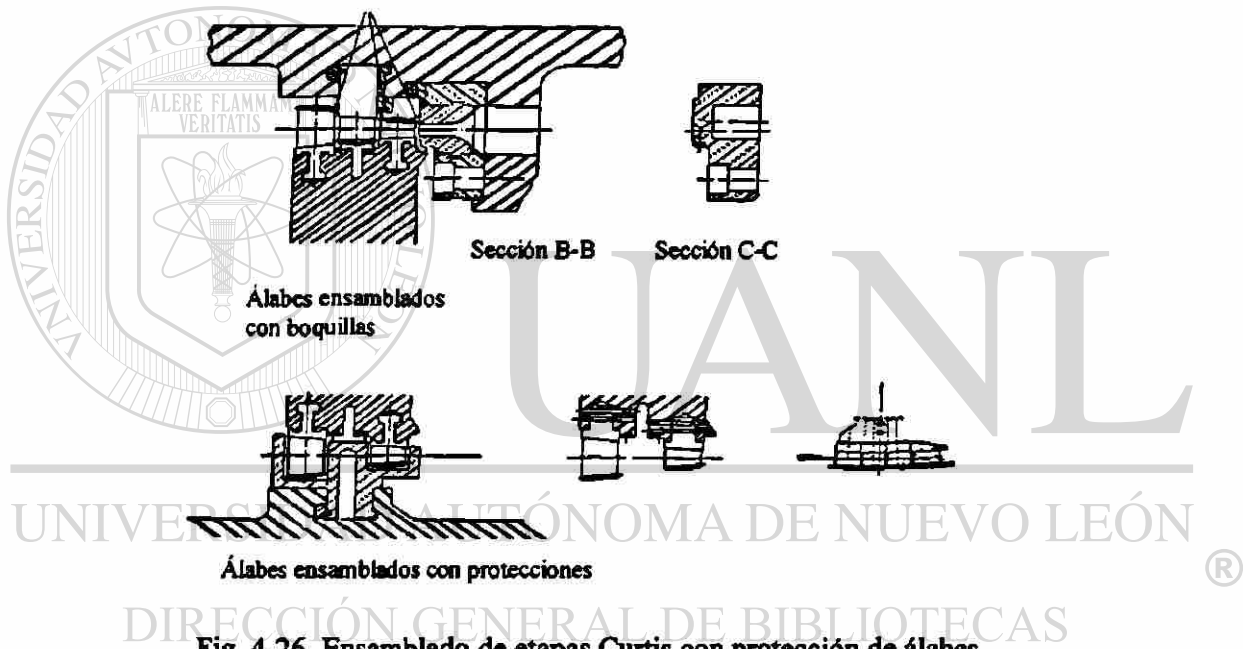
Ensamblado de etapas Curtis con protección de álabes.
